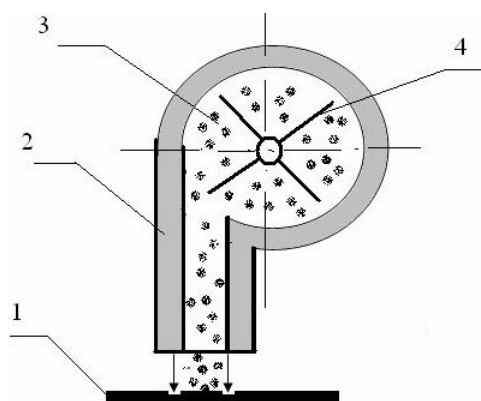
Схема роторного дробемета: 1 – изделие; 2 – корпус дробемета; 3 – дробь чугунная или стальная; 4 – ротор дробемета
